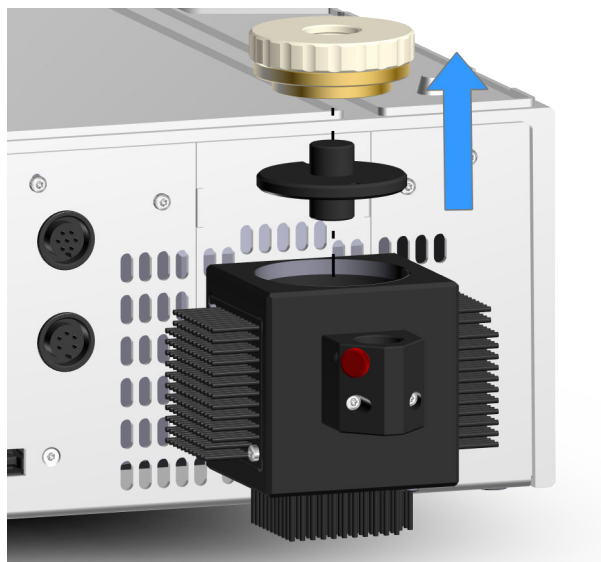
Fassungskappe für die UV-Lampe entfernen
